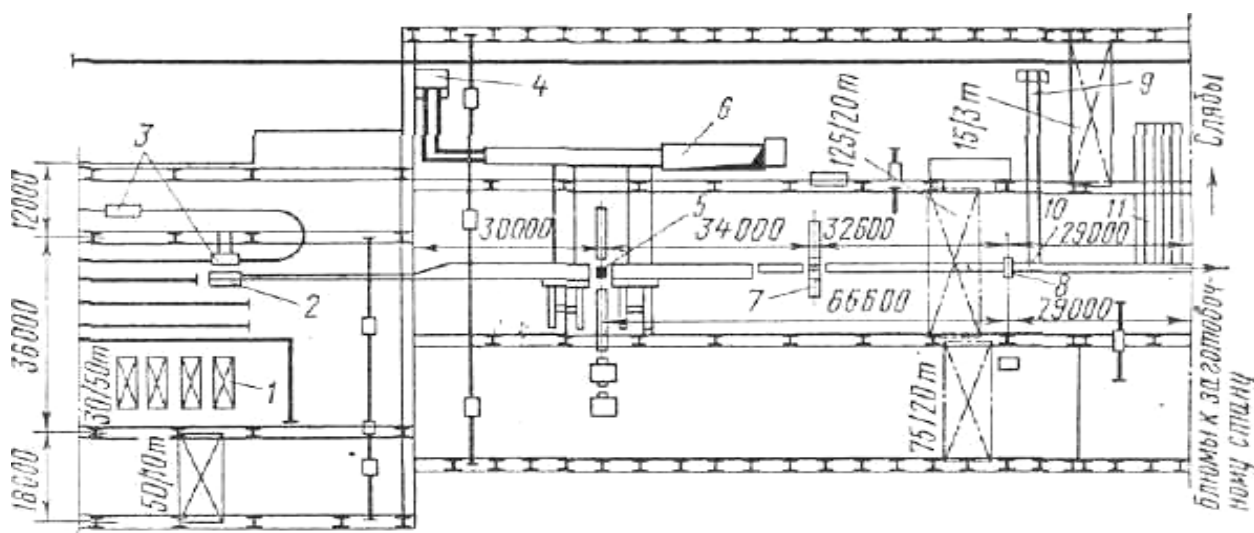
Схема розташування устаткування блємінга 1050 з кільцевим рухом злитковоза: 1 - нагрівальні колодязі; 2 - прийомний рольганг і бічний штовкувач злитків з горизонтальної рами злитковоза; 3 - злитковози; 4 - бункер для зневоднювання окалини і навантаження її в залізничні вагони; 5 - робоча кліть; 6 - колодязь для окалини; 7 - машина для вогневого зачищення блємів; 8 - ножиці з нижнім різанням зусиллям 12 500 кН; 9 - транспортер для обрізків; 10 - рольганг для подачі блємів до безперервного заготовочного стану; 11 - транспортер для слябів
